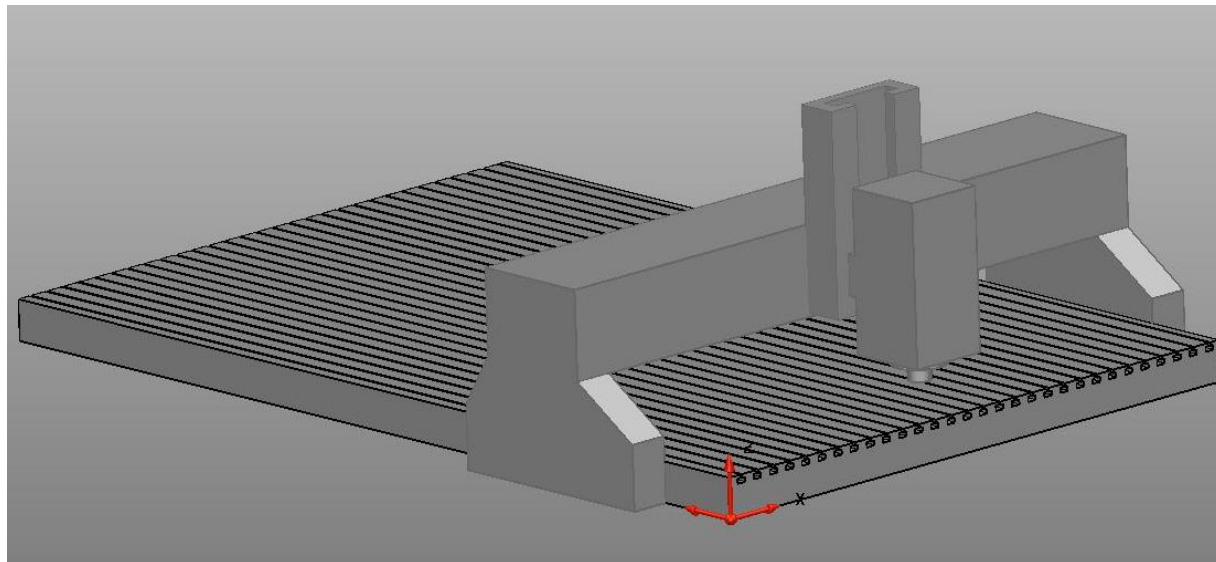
3D модель верстата Woodpecker CAMARO-1208.
